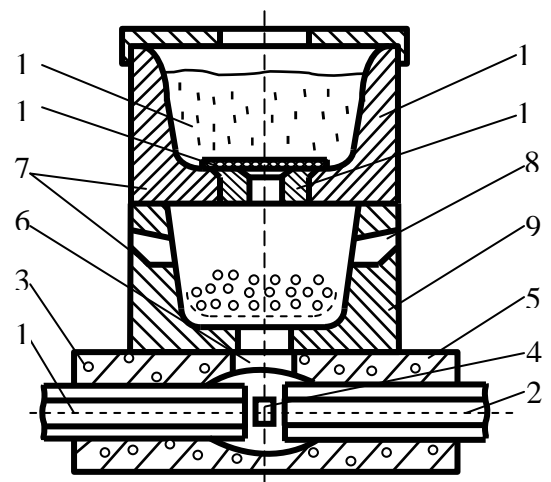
Схема двохкамерного реактору із пристосуванням для зварювання
